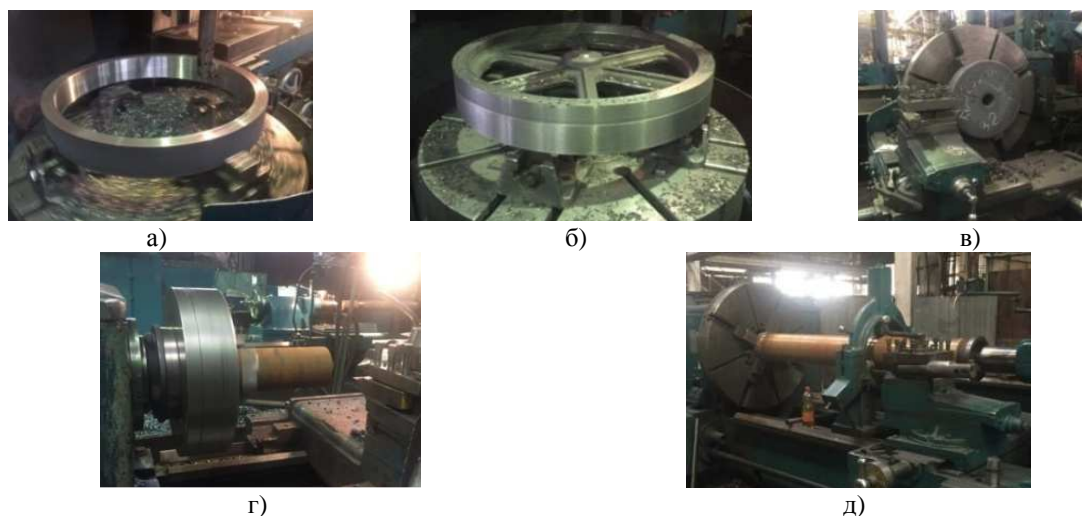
Процессы токарной обработки: а – точение внутренней поверхности зубчатого кольца; б – точение наружной цилиндрической поверхности шкива; в – точение наружной цилиндрической поверхности зубчатого колеса; г, д – точение бочки роликов
